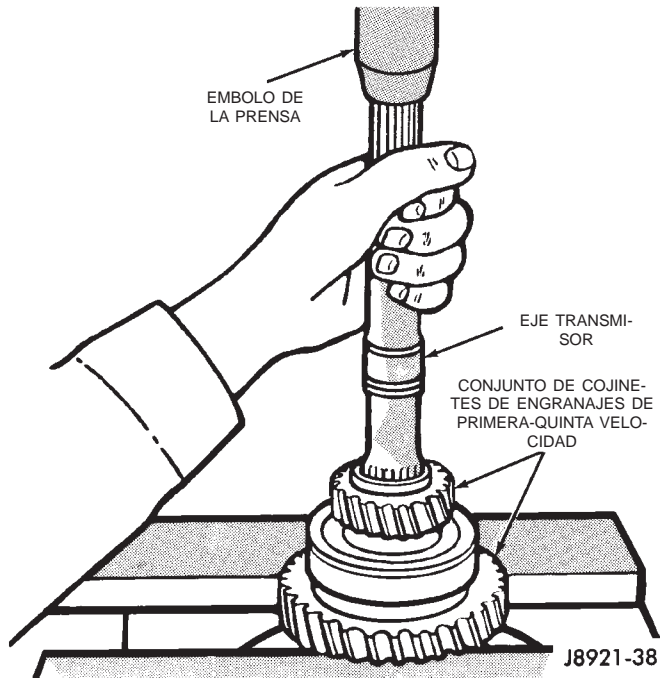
Desmontaje de engranaje de quinta velocidad, cojinete de engranaje de primera velocidad y arandela de empuje
